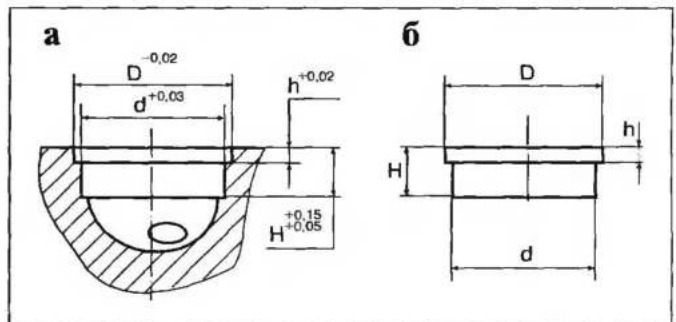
Схема обработки гнезда головки блока дизеля для установки ремонтной вставки (крышки) форкамеры: а — гнездо; б — крышка
